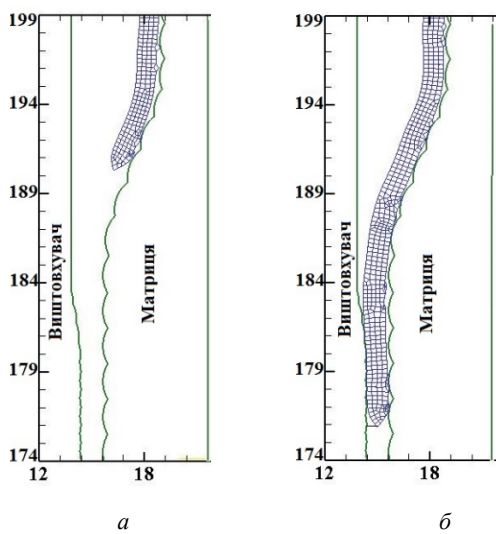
Фрагменти zdeформованої заготовки та інструменту спеціального профілю: а – на конусі, б – в зазорі
